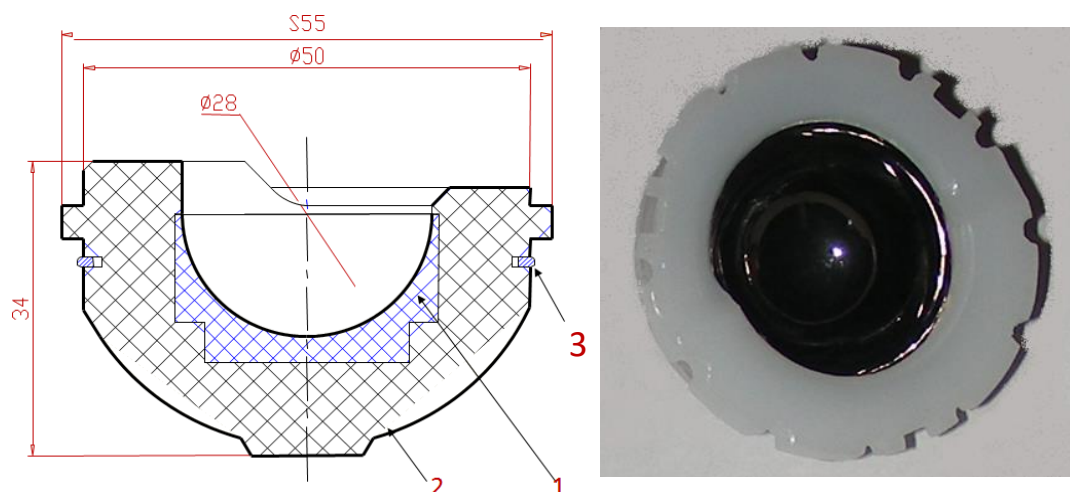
Схема и внешний вид первой конструкции вкладыша из полиэтилена и углеситалла: 1 – вставка из углеситалла; 2 – полиэтиленовый адаптер; 3 – фиксирующее кольцо
